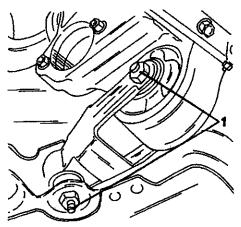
Крепление моментной опоры. Отвернуть гайки (1) с обеих сторон.
